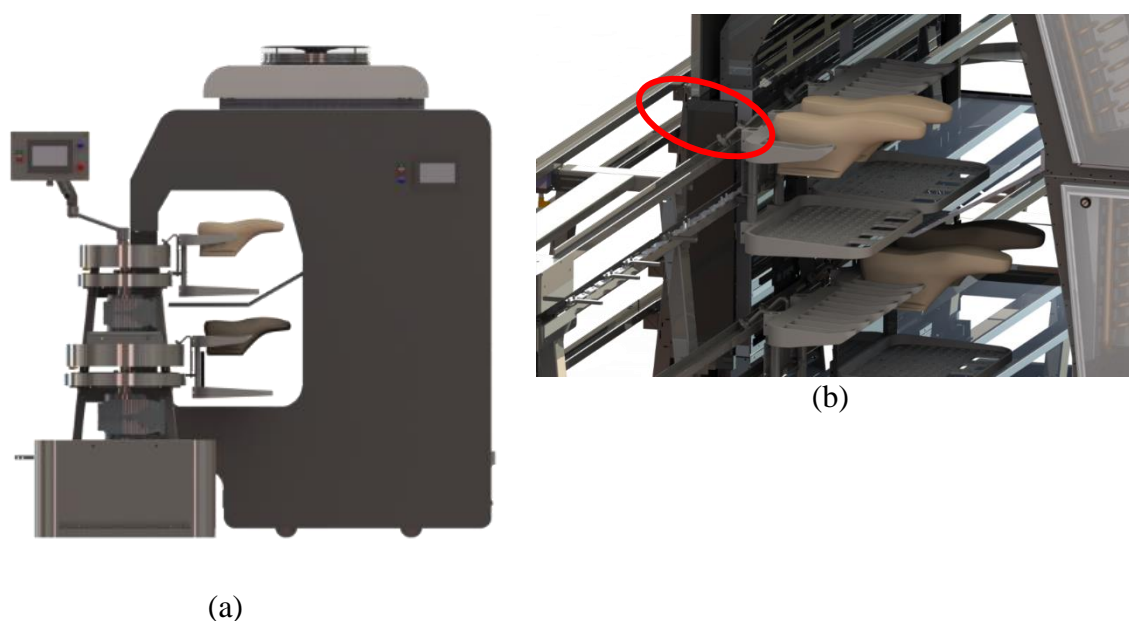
(a) Vista lateral do equipamento montado em trilho (b) Carros com formas no interior do equipamento, em vermelho destacado a exemplificação do tamanho máximo de 50 mm da geometria no centro do trilho.
